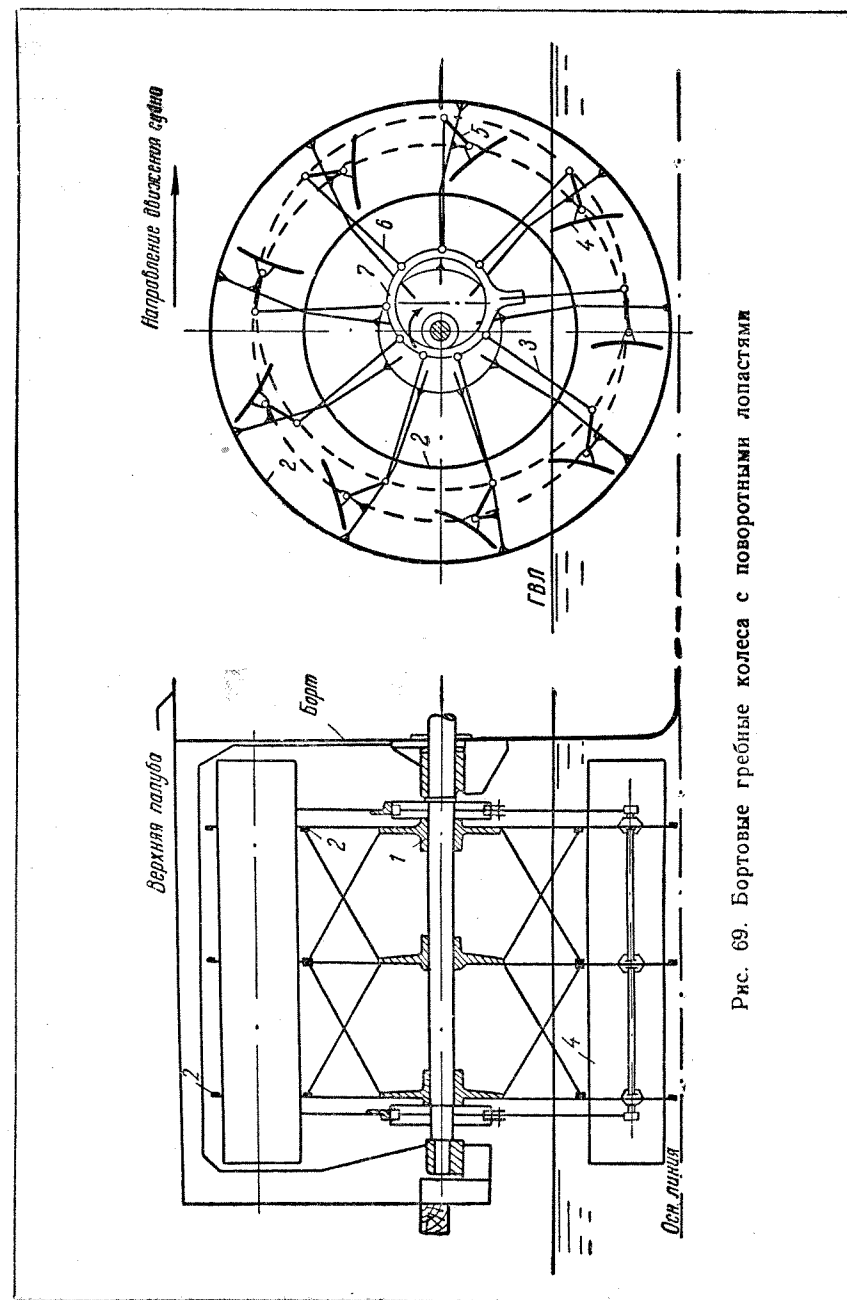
Бортовые гребные колеса с поворотными лопастями
